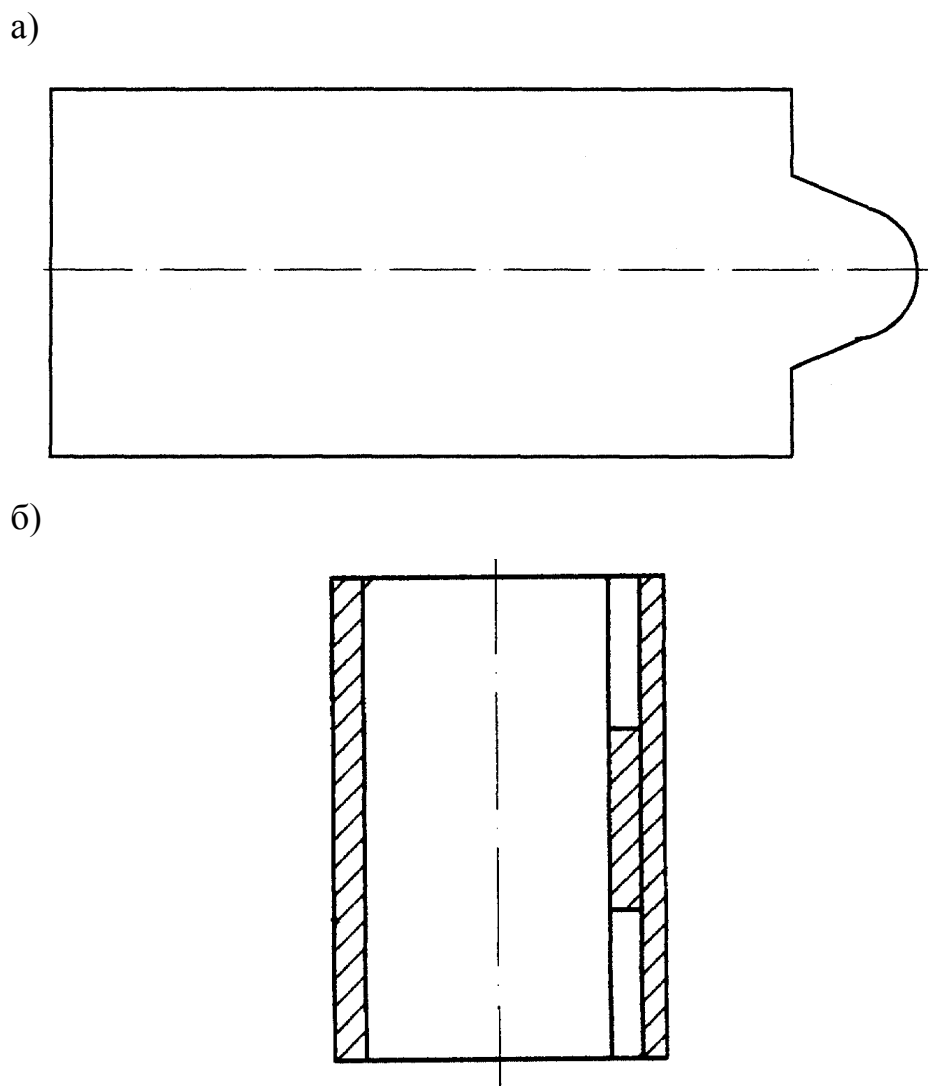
Заготовка под обжим: до свертки (а) и после свертки (б)
